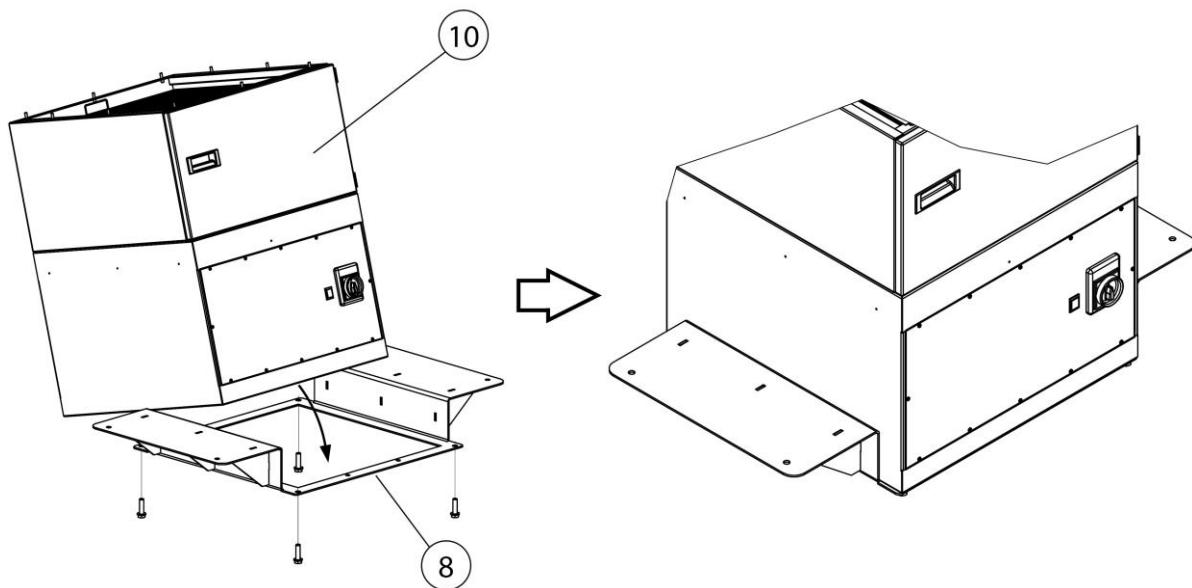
Монтаж – установка фильтровального устройства на опорной раме
